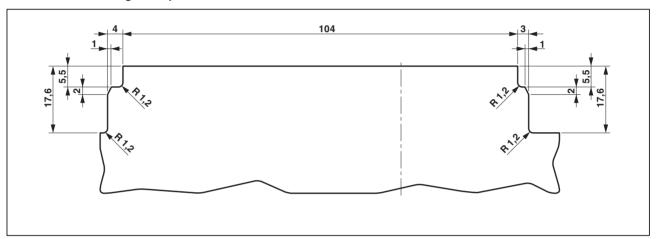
Maßzeichnung der Leiterplatte des Gehäuses bei Verwendung des Universaldeckels CL
